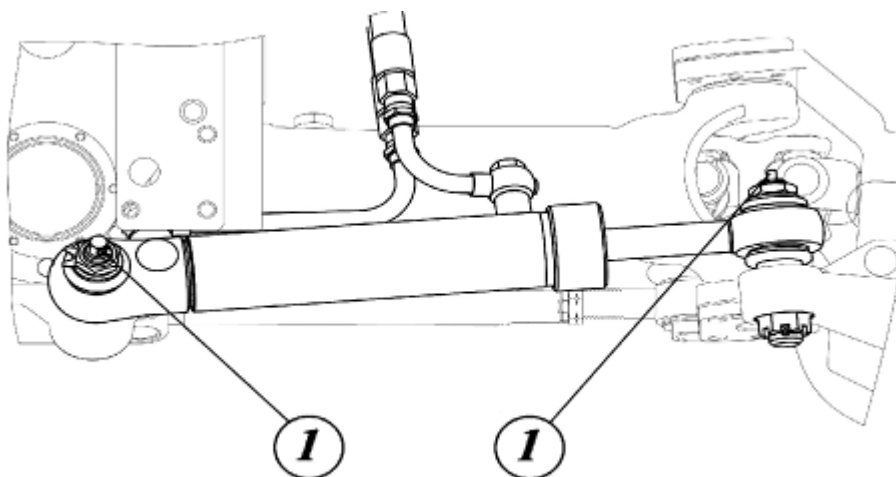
Смазка шарнира гидроцилиндра рулевого управления.
